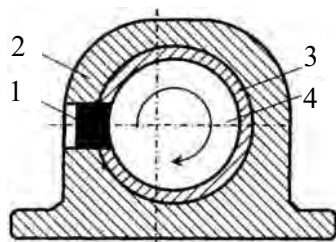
Ротапринтный метод нанесения твердого композиционного смазочного материала скольжением на рабочие поверхности
